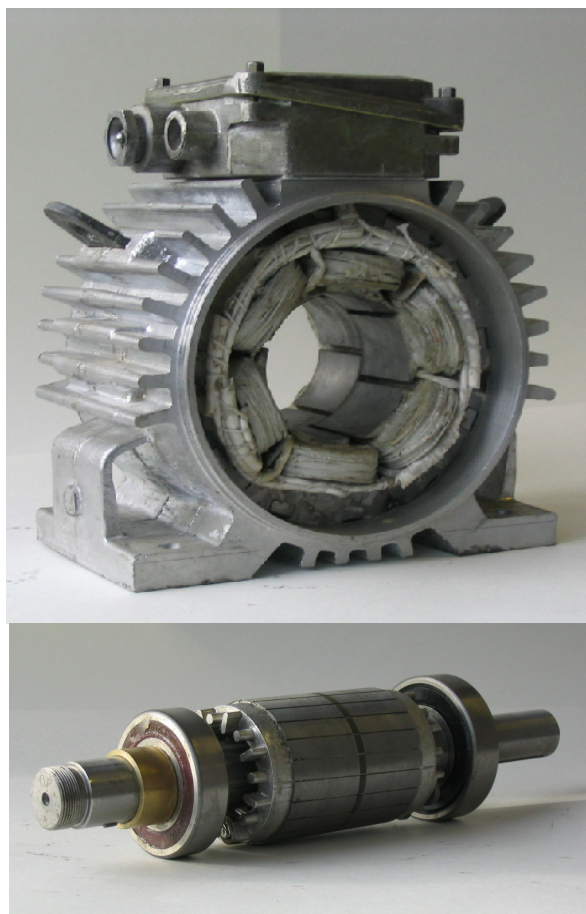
Статор и ротор опытного образца АДАМ новой конструкции
